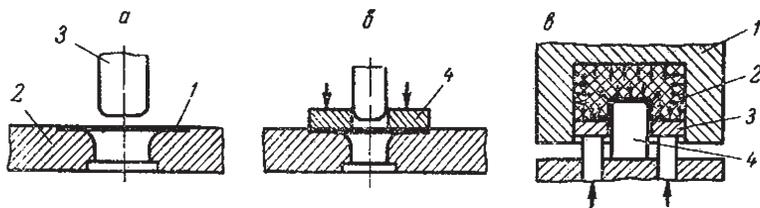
Вытяжка: 1 – заготовка; 2 – матрица; 3 – пуансон;
